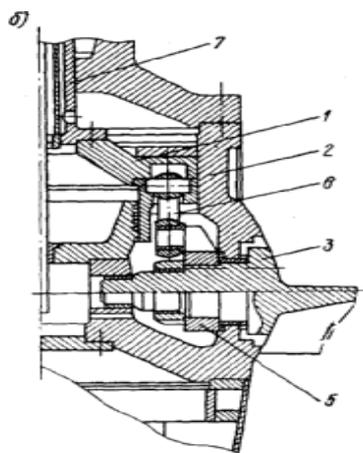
Разрез рабочего колеса с дифференциальным поршнем: 1-дифференциальный поршень; 2-корпус р.к.; 3-лопасть; 4-цапфа; 5-РЫЧАГ; 6-серьга; 7- контршток сервомотора.
